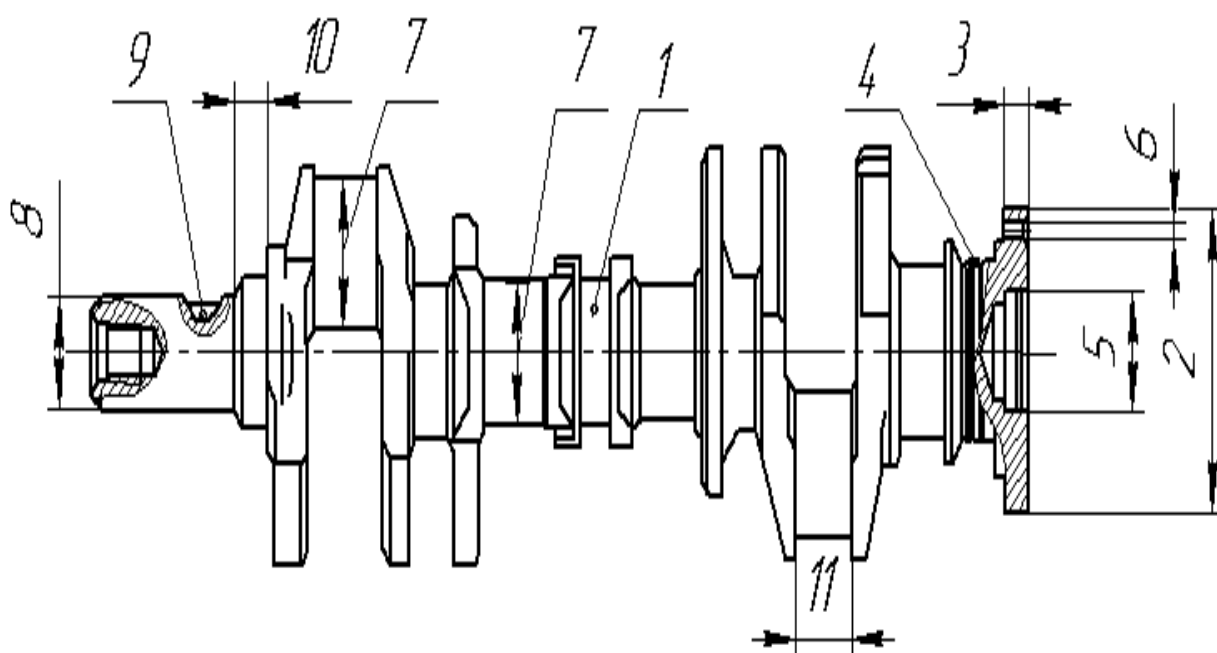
Основные дефекты коленчатого вала на примере двигателя ЗИЛ-130:
